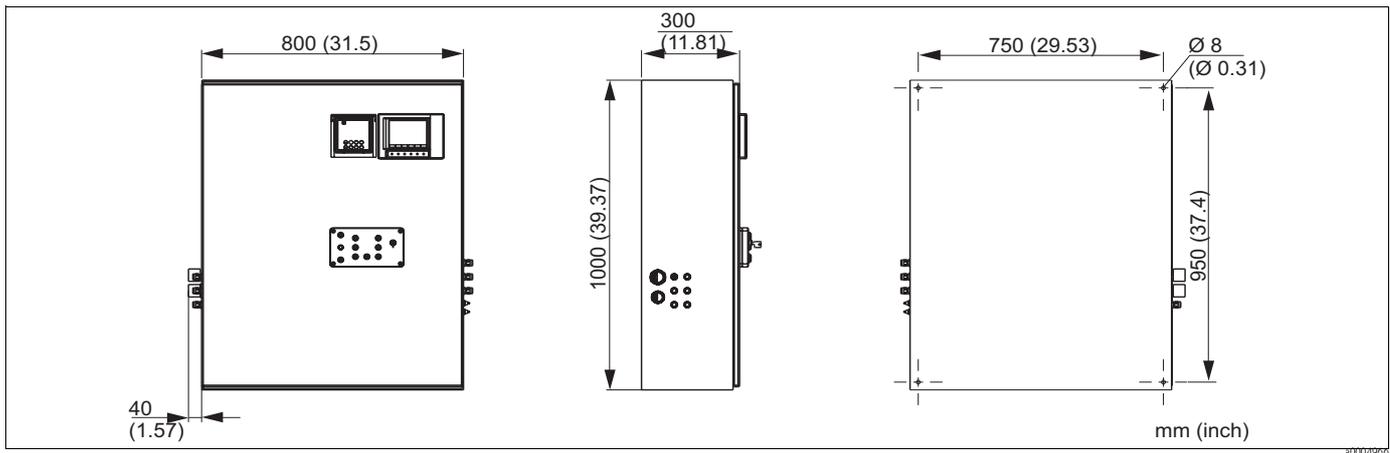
Abmessungen Umschrank CYC310, Kunststoffausführung
